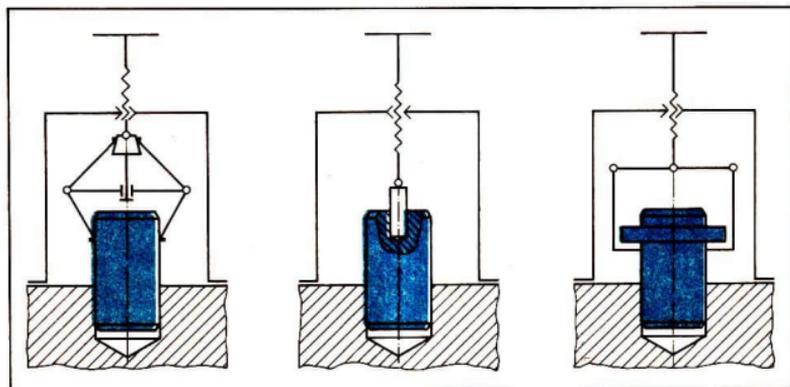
/1 Wirkprinzipien einiger Abziehvorrüchtungen
